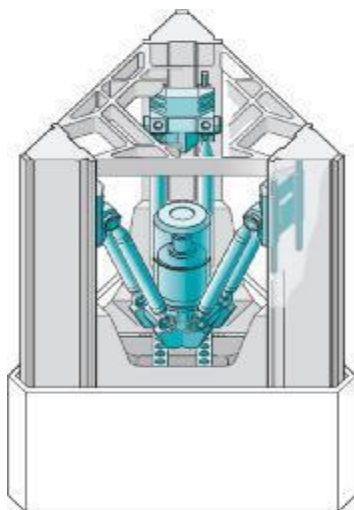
Токарный станок мод. V100 на базе МПС фирмы Index-Werke (ФРГ)
